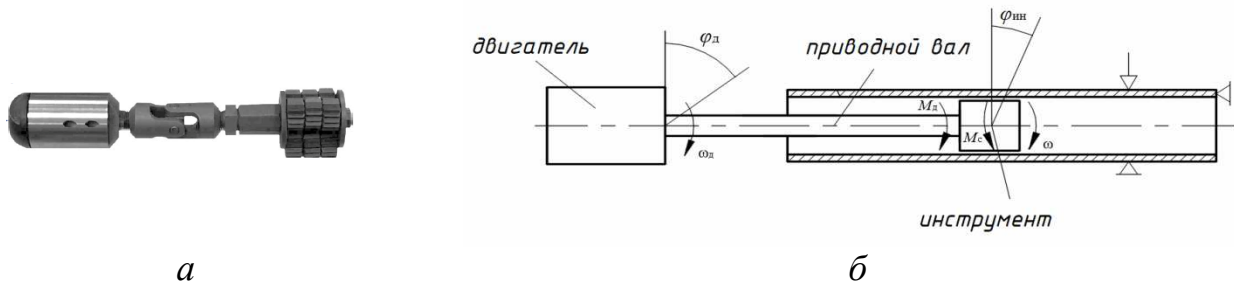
Устройство для отчистки теплообменных труб: а – рабочий инструмент установки; б – расчетная схема
